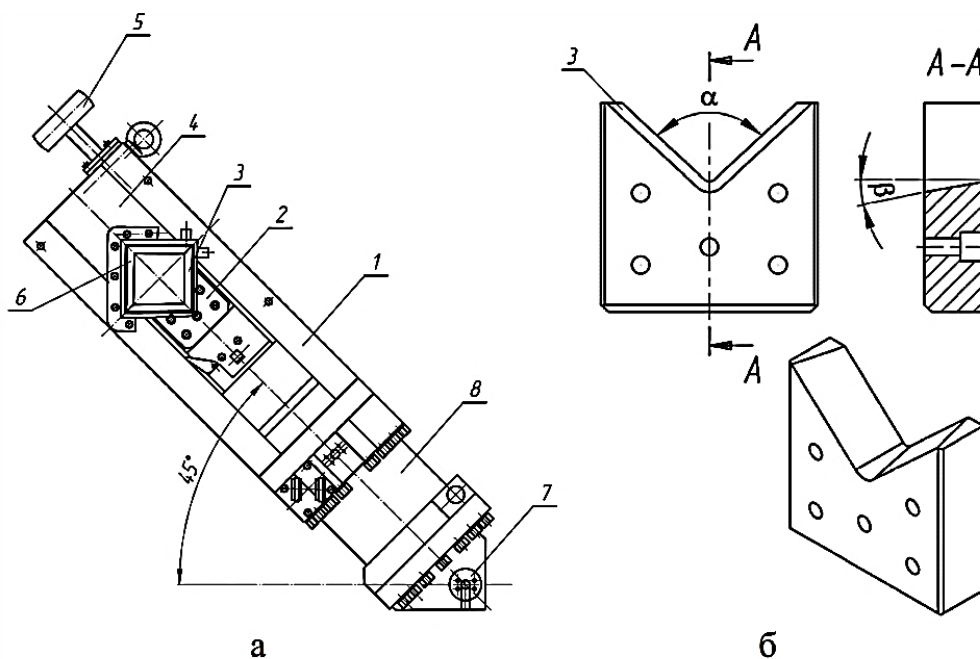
Общий вид (а) ножниц летучих гидравлических конструкции НКМЗ для поперечной горячей резки на мерные длины непрерывно-литых квадратных заготовок и профилировка ножа (б):
